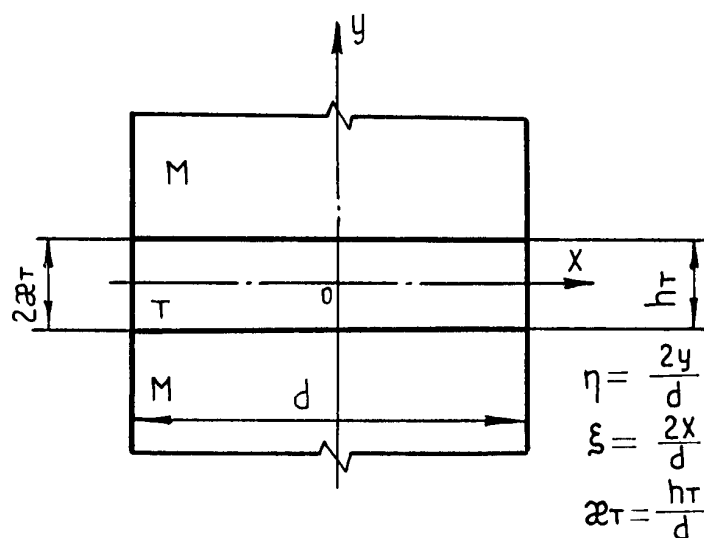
Схема сварного соединения с твердой прослойкой
